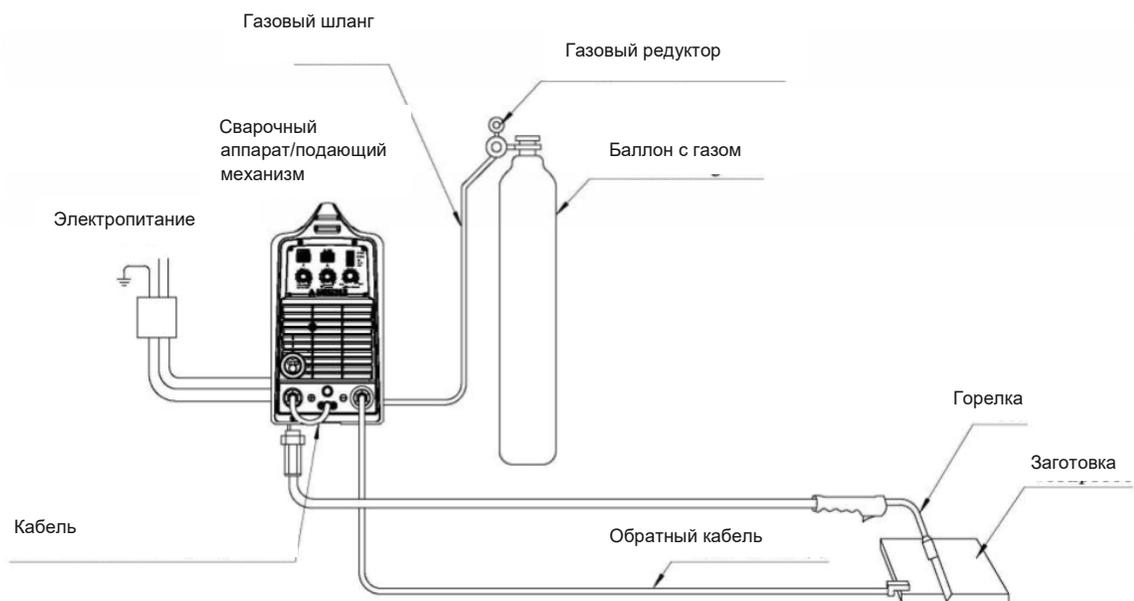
MIG/MAG сварка проволокой из углеродистой стали
